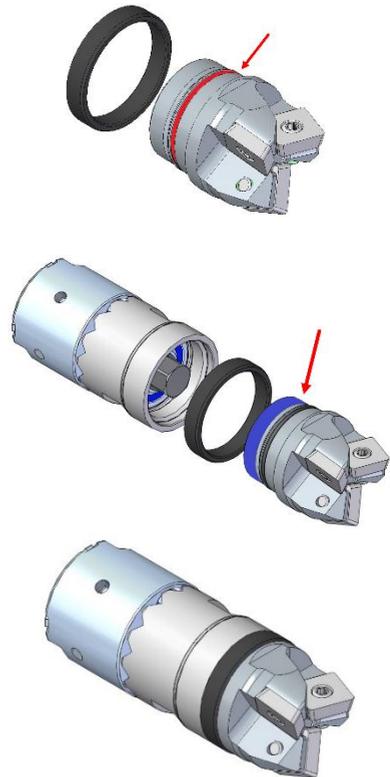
Umbau auf Fräser ohne Schlag
